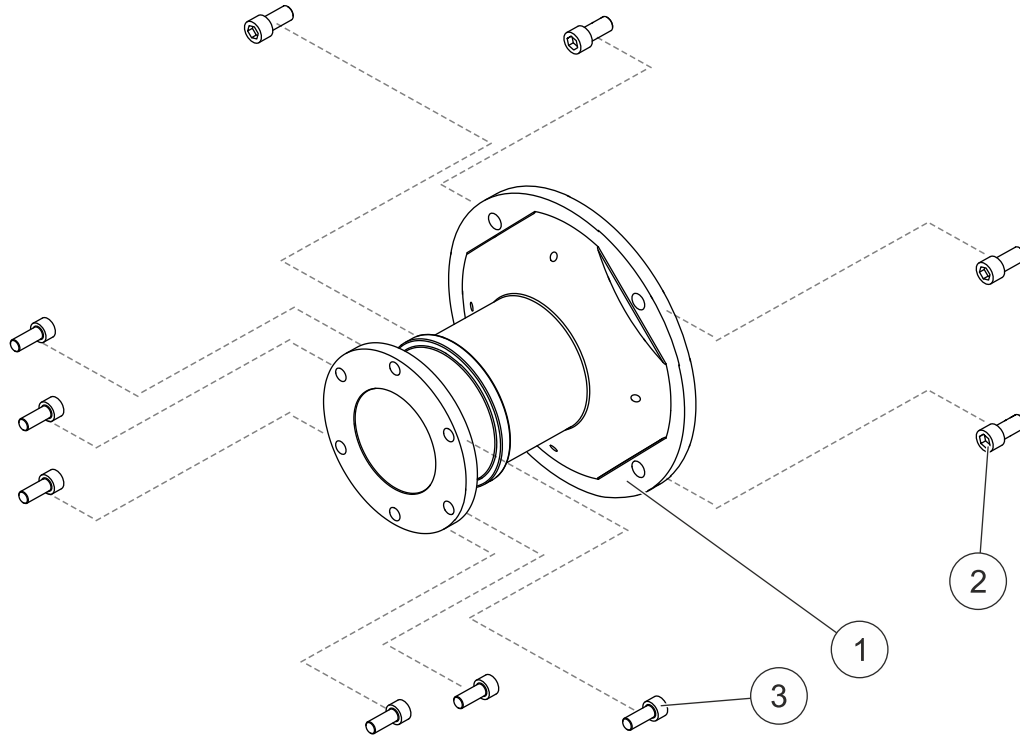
Baugruppe Motorflansch PQ10T-EX
